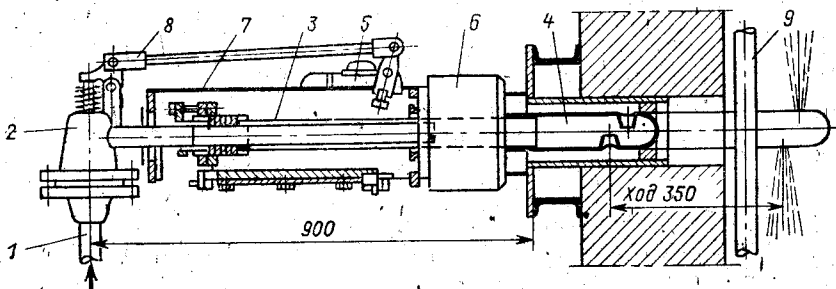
Маловыдвижной обдувочный аппарат типа ОМ-0,35: 1 — подвод пара; 2 — клапан; 3 — шпиндель; 4 — обдувочная головка с двумя соплами Лавалья диаметром 20 мм; 5 — электродвигатель; 6 — редуктор; 7 — корпус; 8 — рычажный механизм привода клапана; 9 — экранная труба
